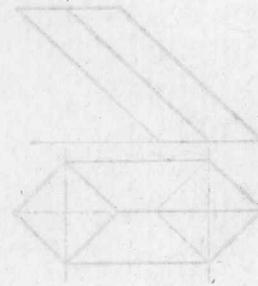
13 圆柱形零件的三视图：主视图表示该零件的两个端面和一个侧面。
